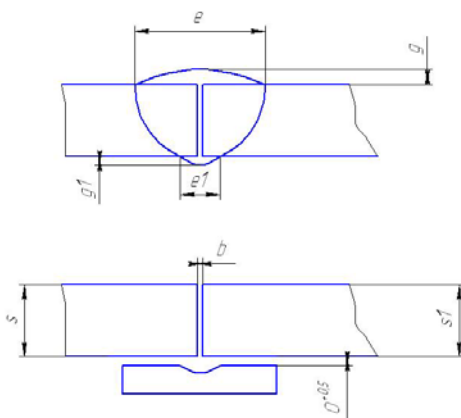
Параметры сварного шва С4 по ГОСТ 14771-76
